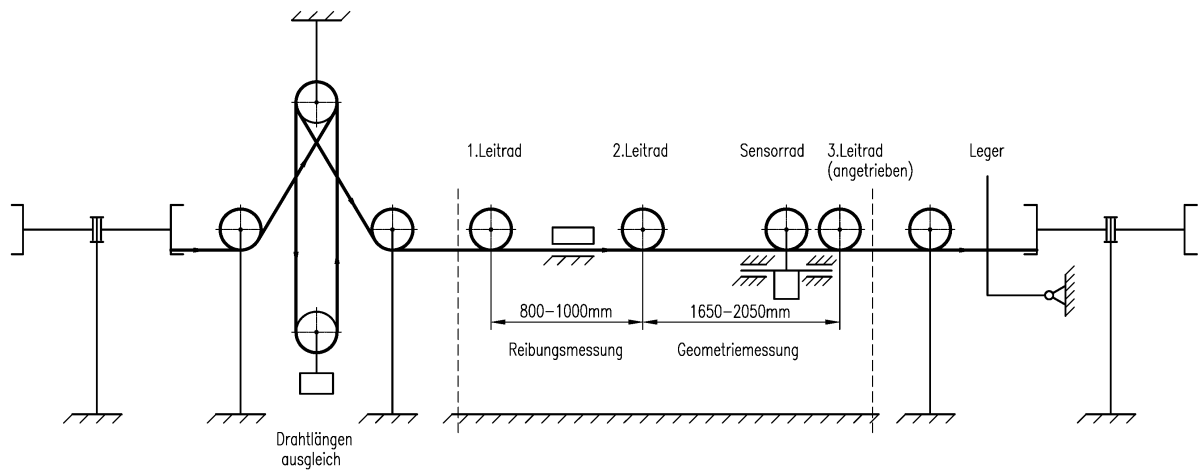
Drahtprüfeinrichtung für Drähte mit  $1,0 \text{ mm} \leq d \leq 2,0 \text{ mm}$
